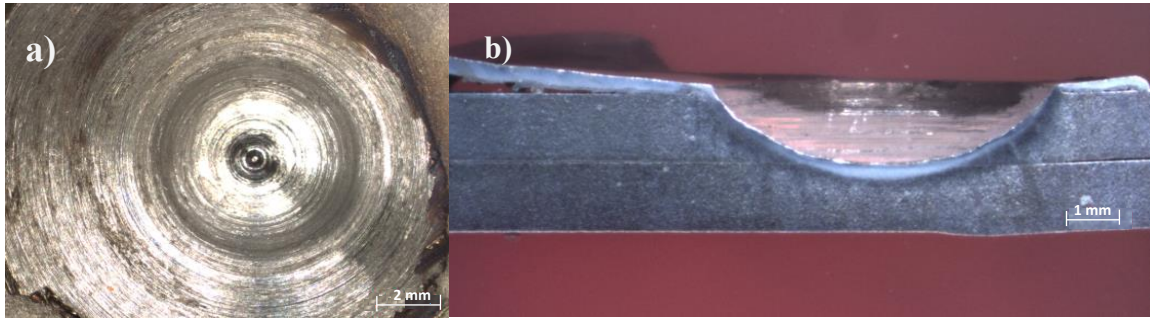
Punto de soldadura por proceso FSSW con parámetros de proceso de 500 RPM y 120 mm/min. a) Vista superior de la unión, b) Perfil transversal de la unión.
